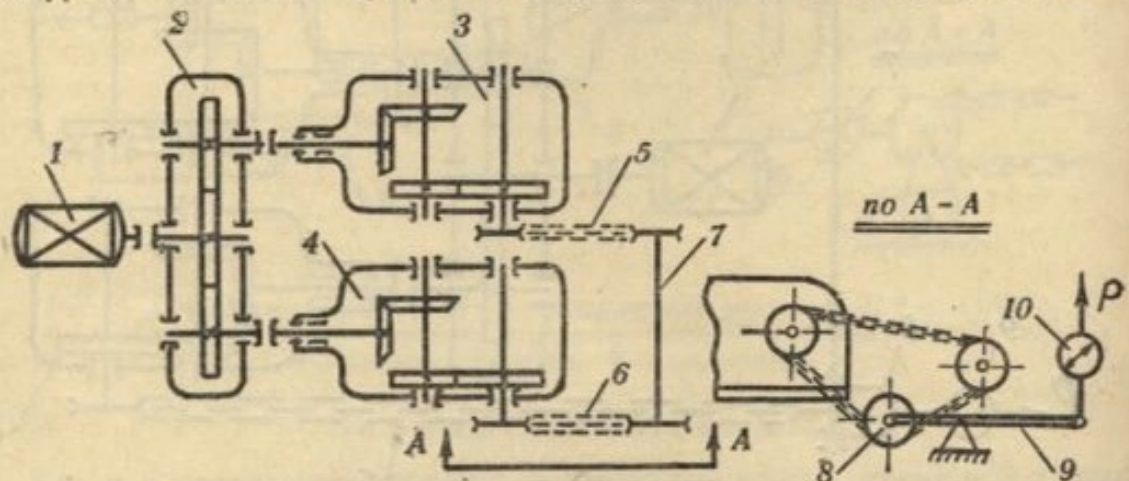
1 — Электродвигатель, 2 — цилиндрический редуктор, 3, 4 — испытуемые редукторы, 5, 6 — втулочно-роликовая цепь, 7 — промежуточный вал, 8 — звёздочка, 9 — рычаг, 10 — динамометр.
